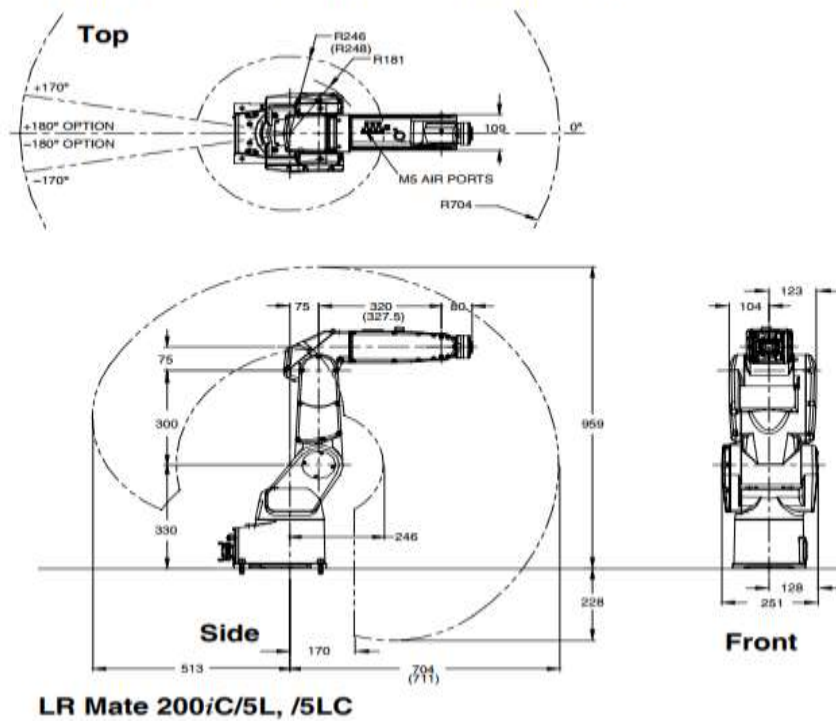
Dimensiones LR Mate iC Fuente: Fanuc Robotics
